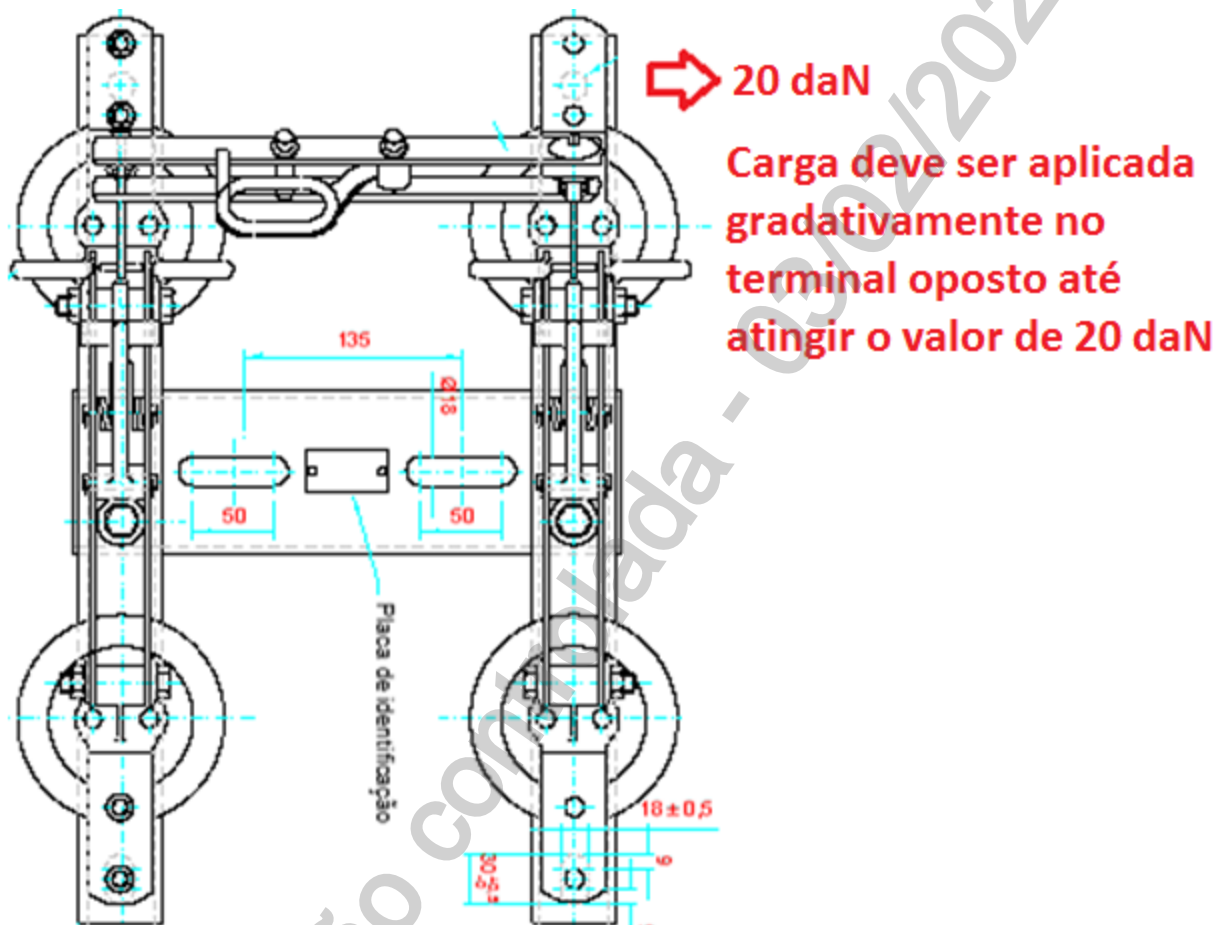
1ª etapa do ensaio item 4.3.4 b), aplicado somente a chaves tipo By-pass
